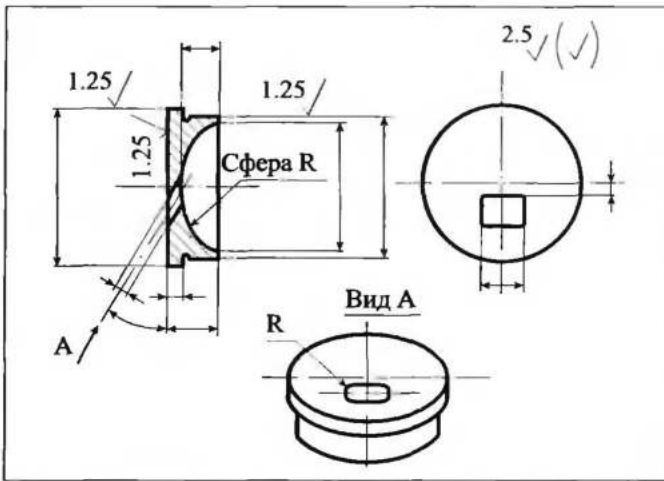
Эскиз вставки (крышки) форкамеры дизельного двигателя
